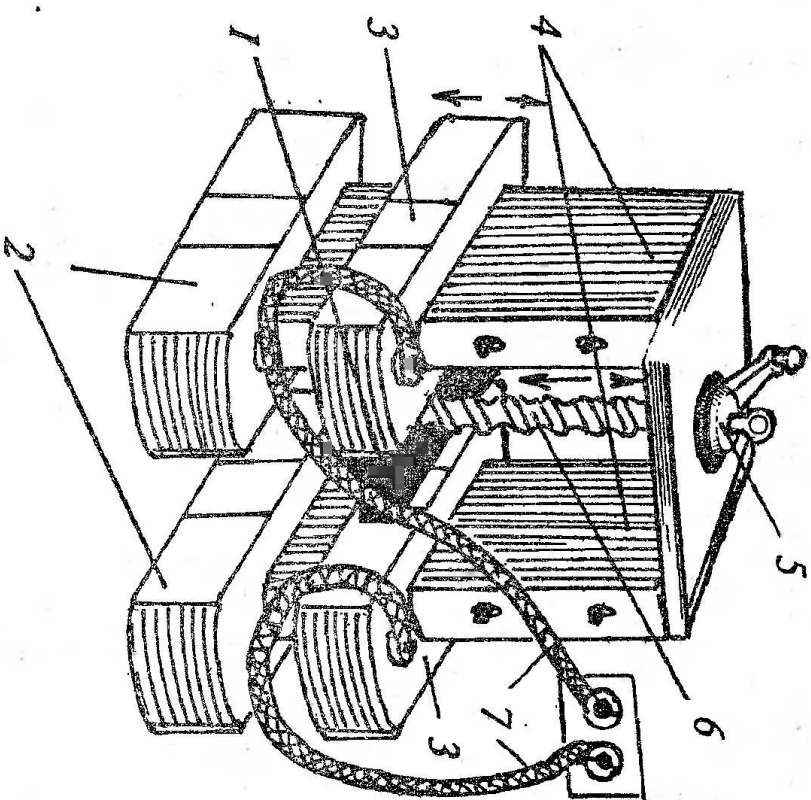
Сварочный трансформатор ТСК-500
